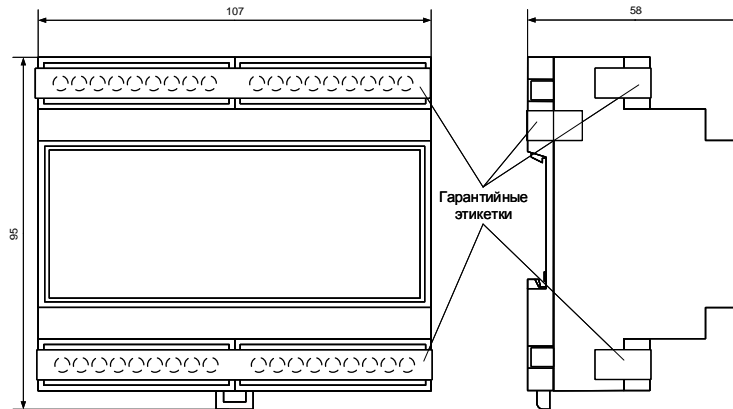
Внешний вид, габаритные и установочные размеры счетчика СИПУ xxx.16.D
